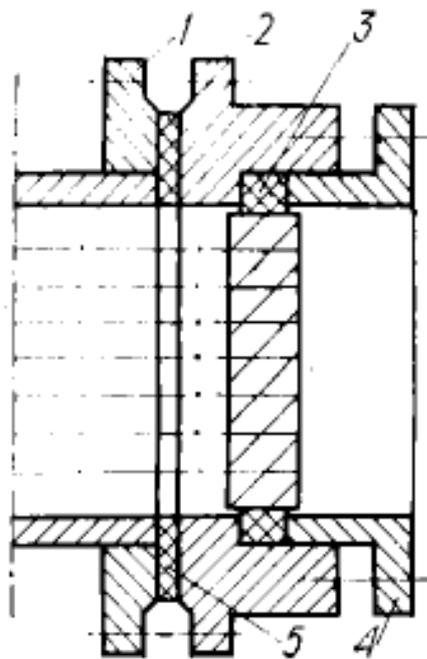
Сальниковое приспособление для опрессовки: 1 – корпус; 2 – фланец; 3 – сальниковая прокладка; 4 – нажимная втулка; 5 – прокладка.
